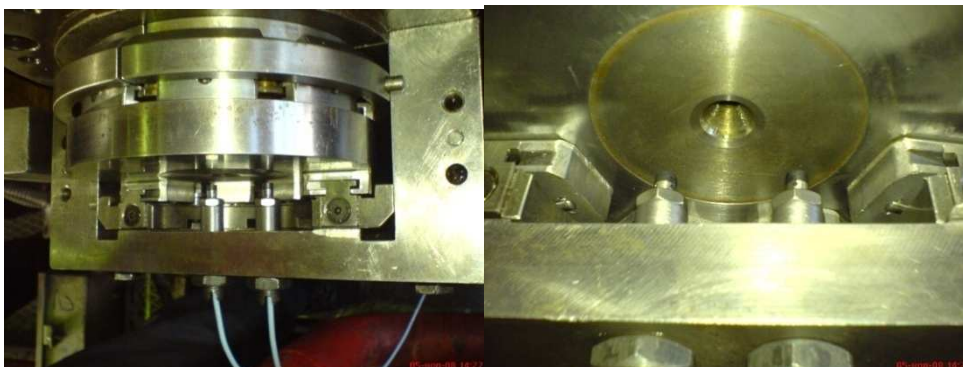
Смонтированные датчики осевого сдвига вал-шестерни мультипликатора компрессора поз.101J
